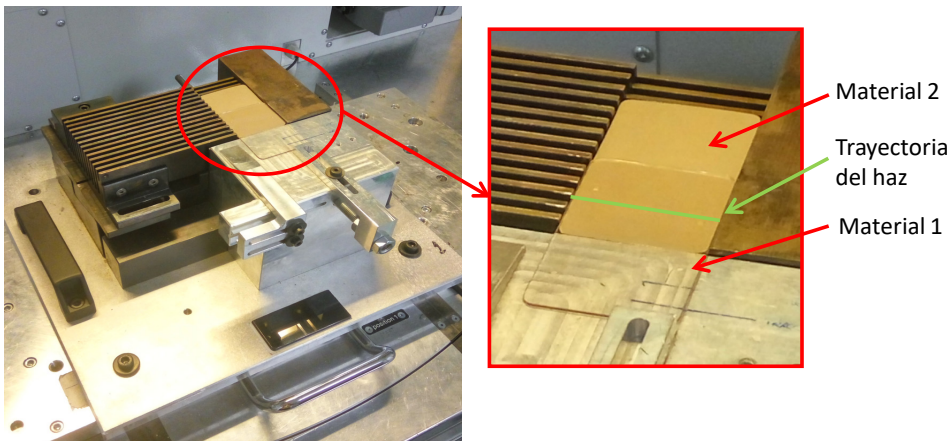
Detalle del utillaje de posicionamiento y fijación de los elementos a soldar.
